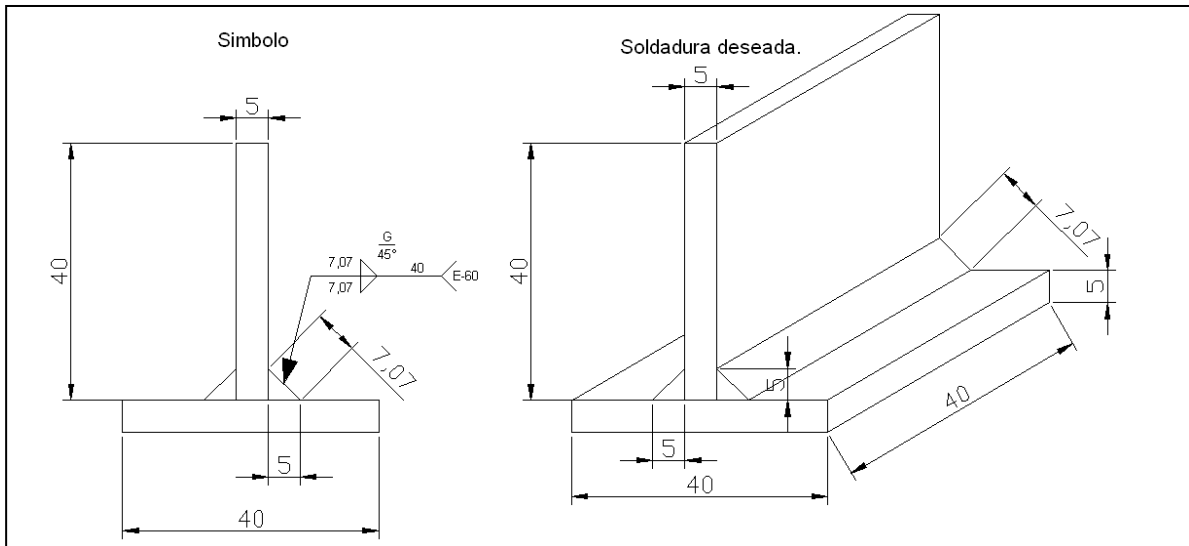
Ejemplo de pieza de acero soldada con terminado de esmerilado (G), de dos filetes iguales 7,07, con soldadura eléctrica para acero= E-60 y 40 cm. de longitud, 45° de inclinación de la soldadura= 7,07cm. Diagrama de soldadura deseada y símbolo de esta.
